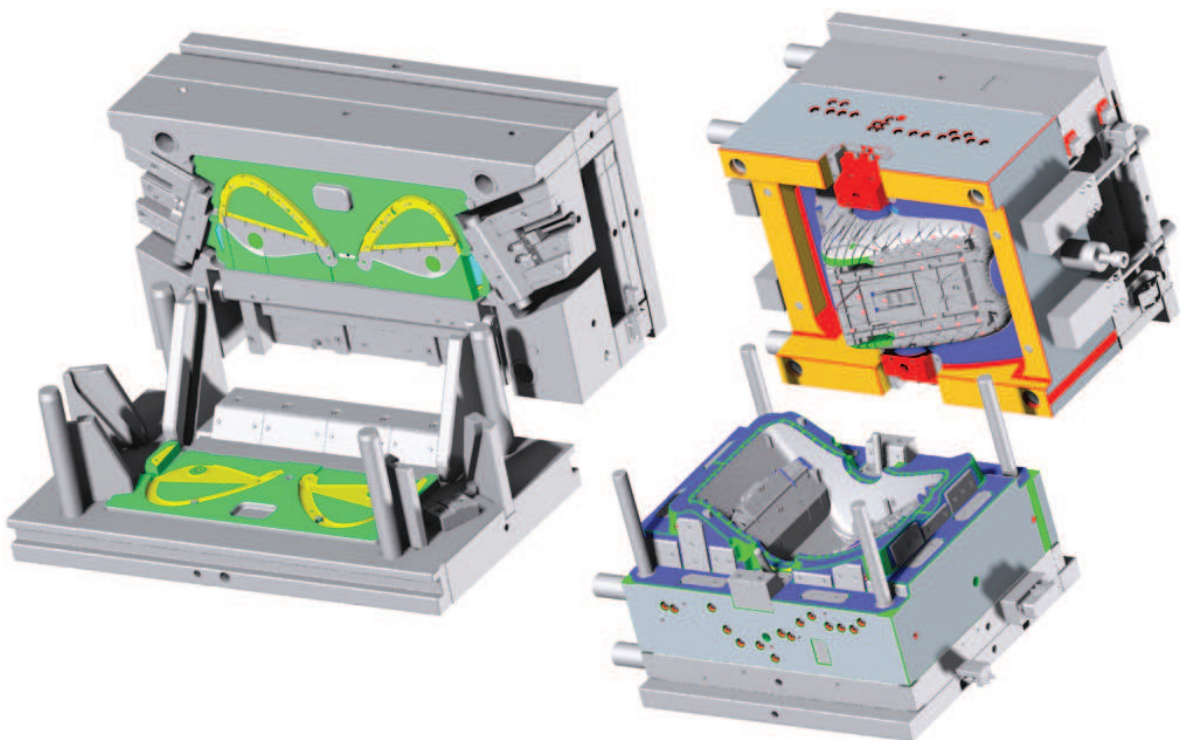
Exemplos típicos de moldes de injeção: molde de canais (esq.) e molde de canais quentes (dir.).
